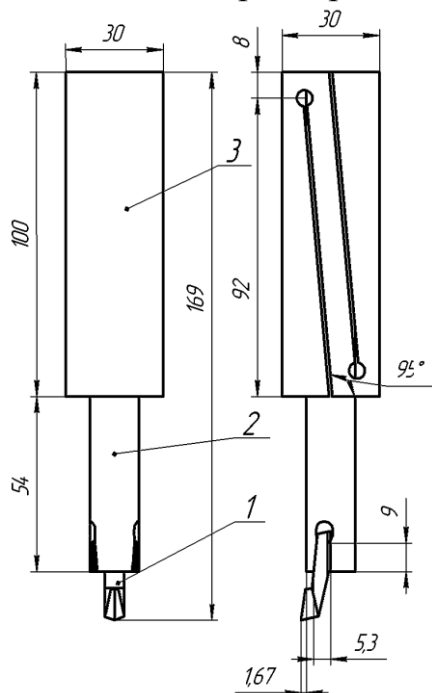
Сборный долбежный резец с установленной вставкой
